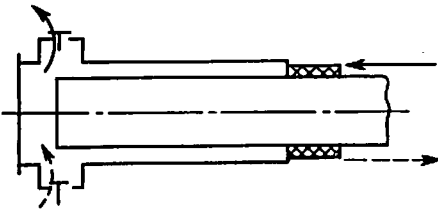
Einfachwirkende Pumpe mit Tauchkolben
